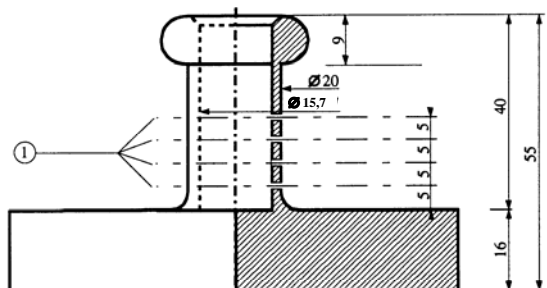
Полый бронзовый цилиндр, закрытый с одной стороны; чертеж и размеры детали в мм
